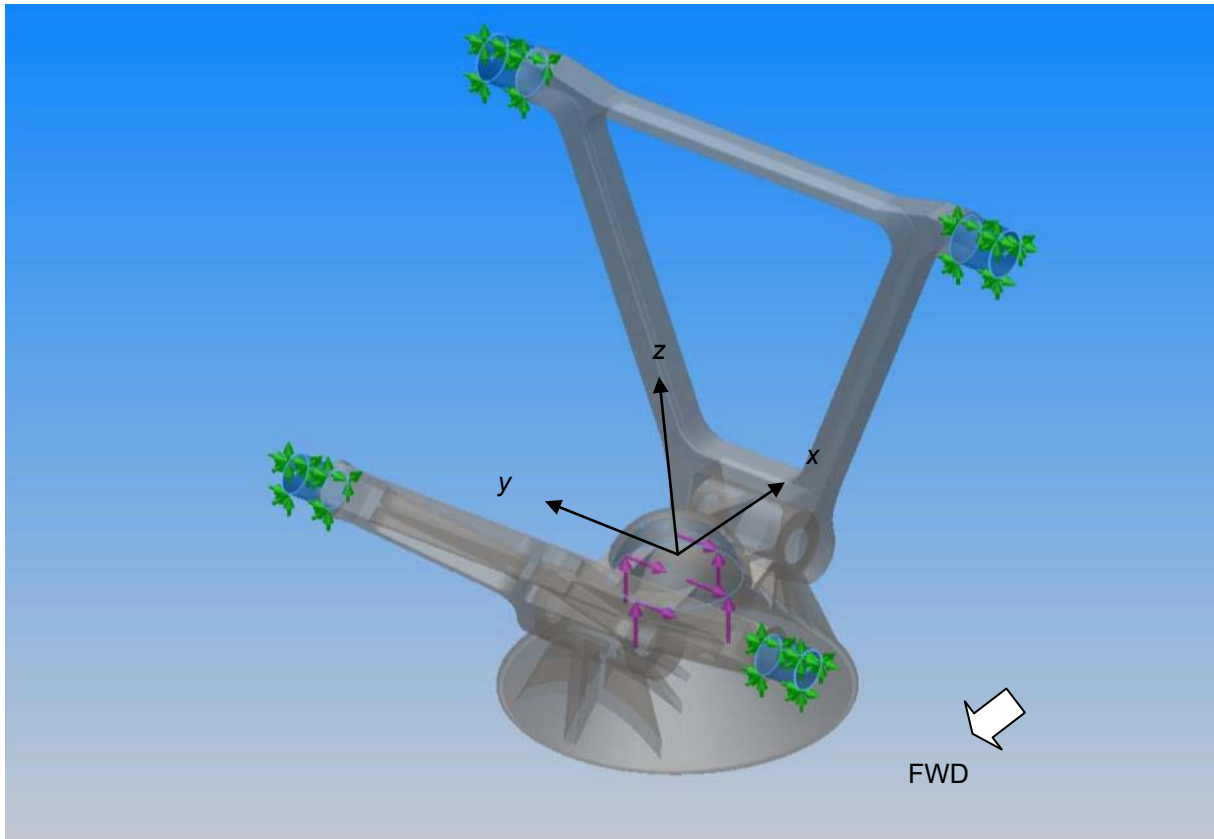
Last- und Lagerdefinition bei der Schnittstelle Rumpffahrwerk
